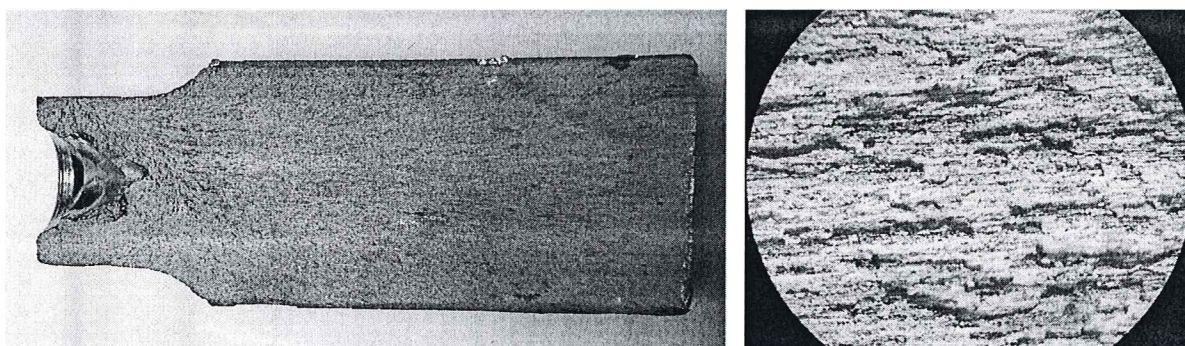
Разрушение прутка из сплава АМг6 и поверхность излома, 16^х.
